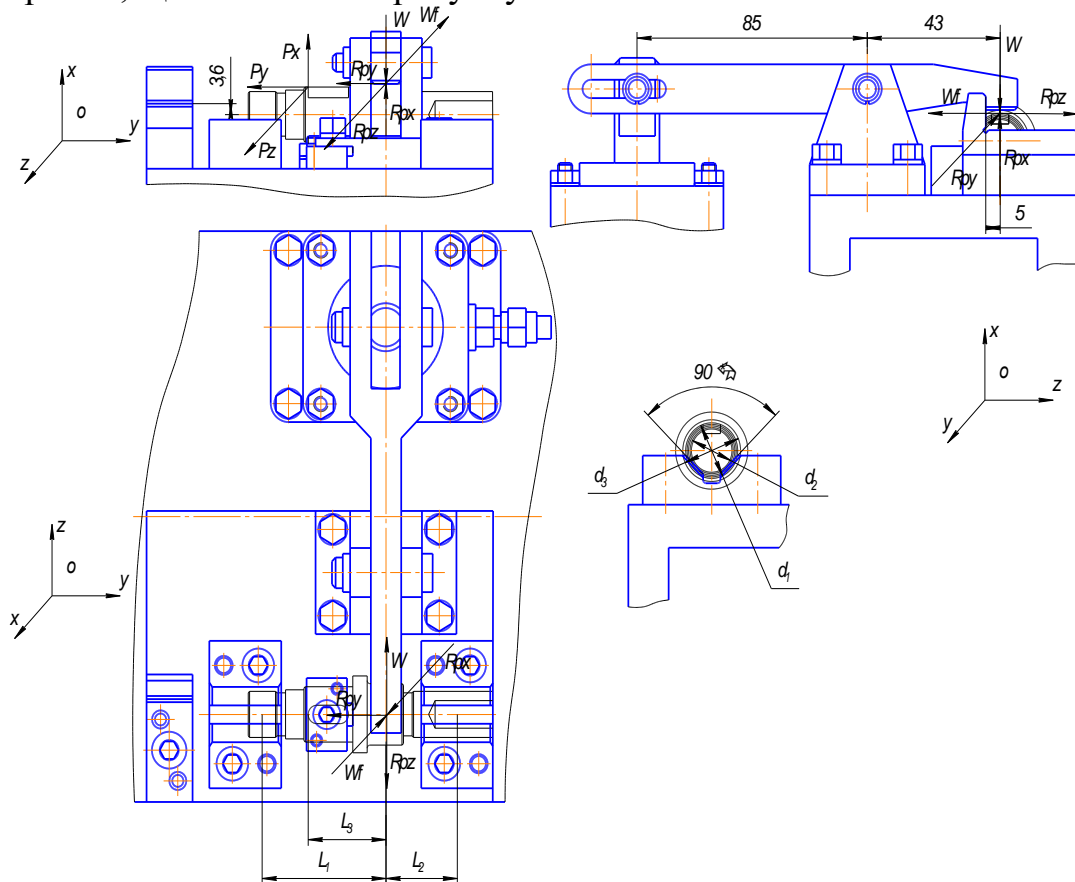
Схема визначення дії зусиль на вал під час фрезерування пазів
